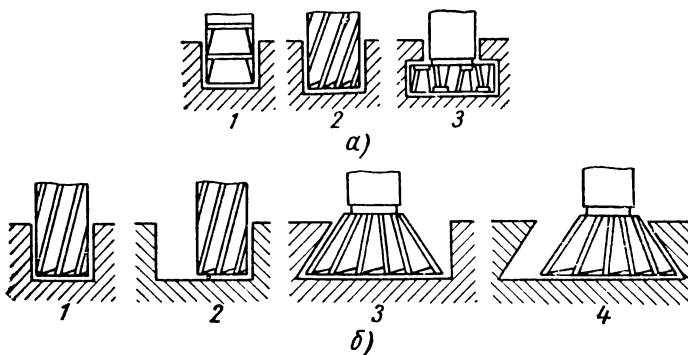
Схема и последовательность фрезерования пазов: а — Т-образных; б — в виде ласточкина хвоста
